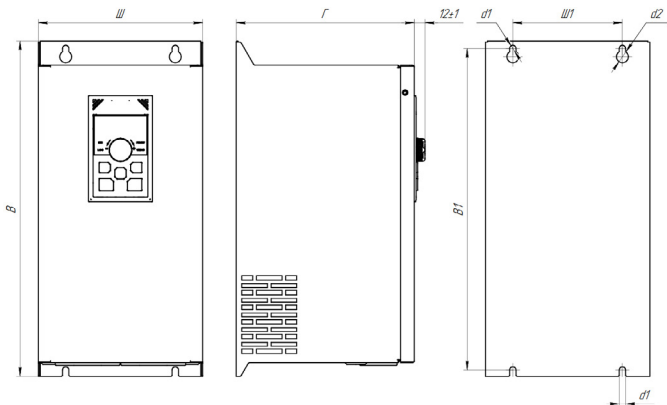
Установочные и габаритные размеры тормозного модуля BU, типоразмер 2
